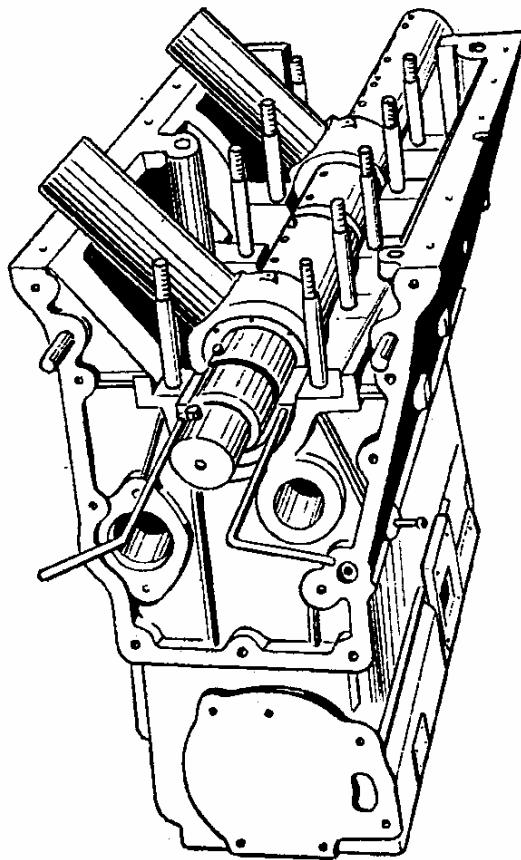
Блок циліндрів з встановленою борштангою (з опорами) на установочних вкладиших
